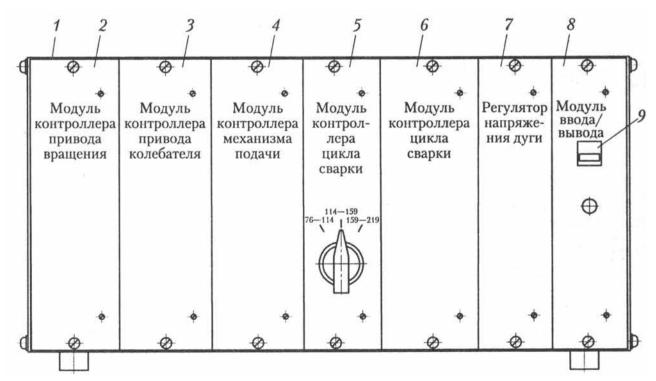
Внешний вид блока интерфейса АДЦ 628.20.00.000: 1 – корпус; модули контроллеров: 2 - привода колебателя; 3 - привода колебателя; 4 - привода подачи присадочной проволоки; 5, 6 - цикла сварки; 7 –автоматического регулятора напряжения дуги (АРНД); 8 – модуль ввода/вывода; 9 – USB-розетка
